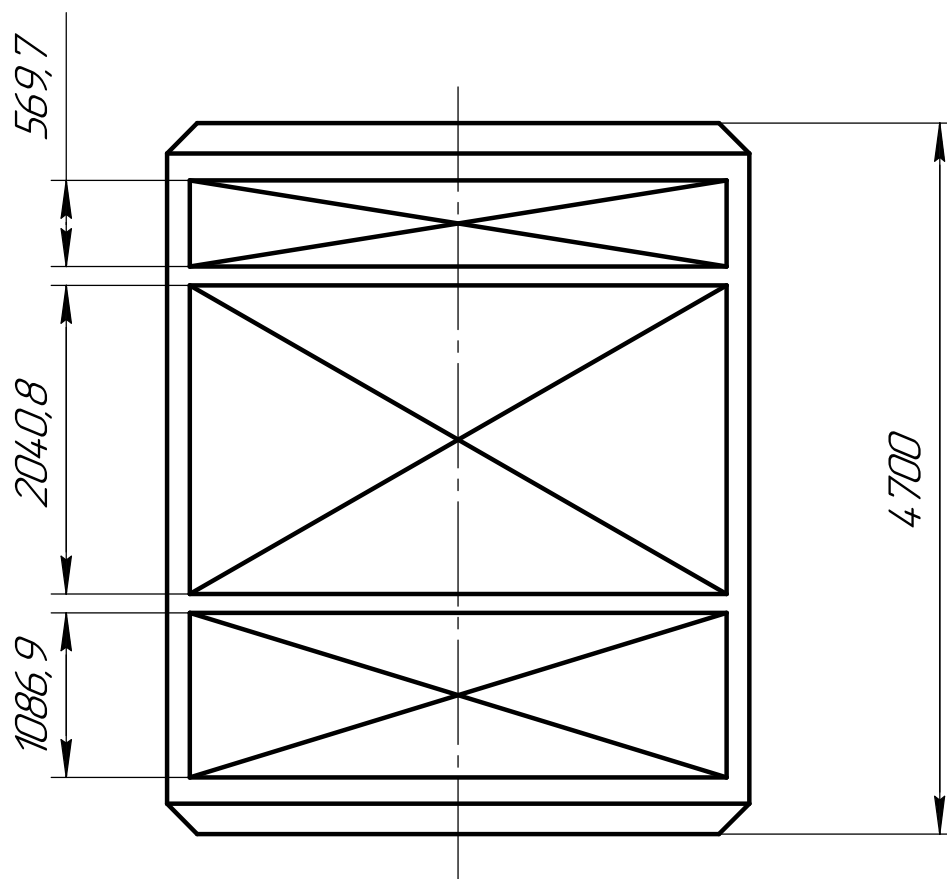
Габаритно-компоновочний ескіз проточної частини УПГ
